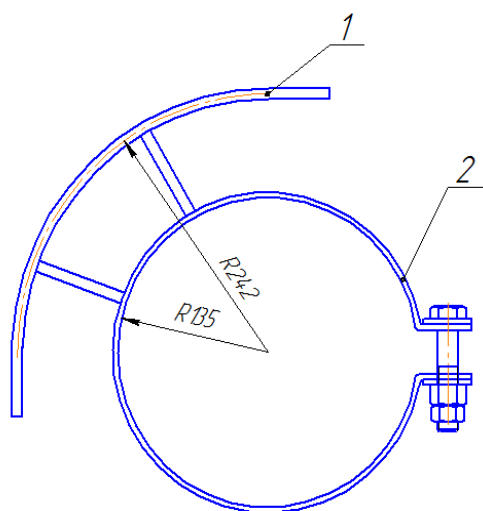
Направляющая пластина с хомутом крепления к пневмоцилиндру
